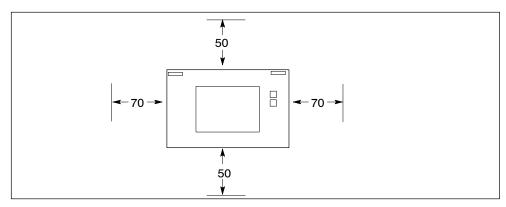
Abstandsmaße beim Einbau des C7-635 Touch
